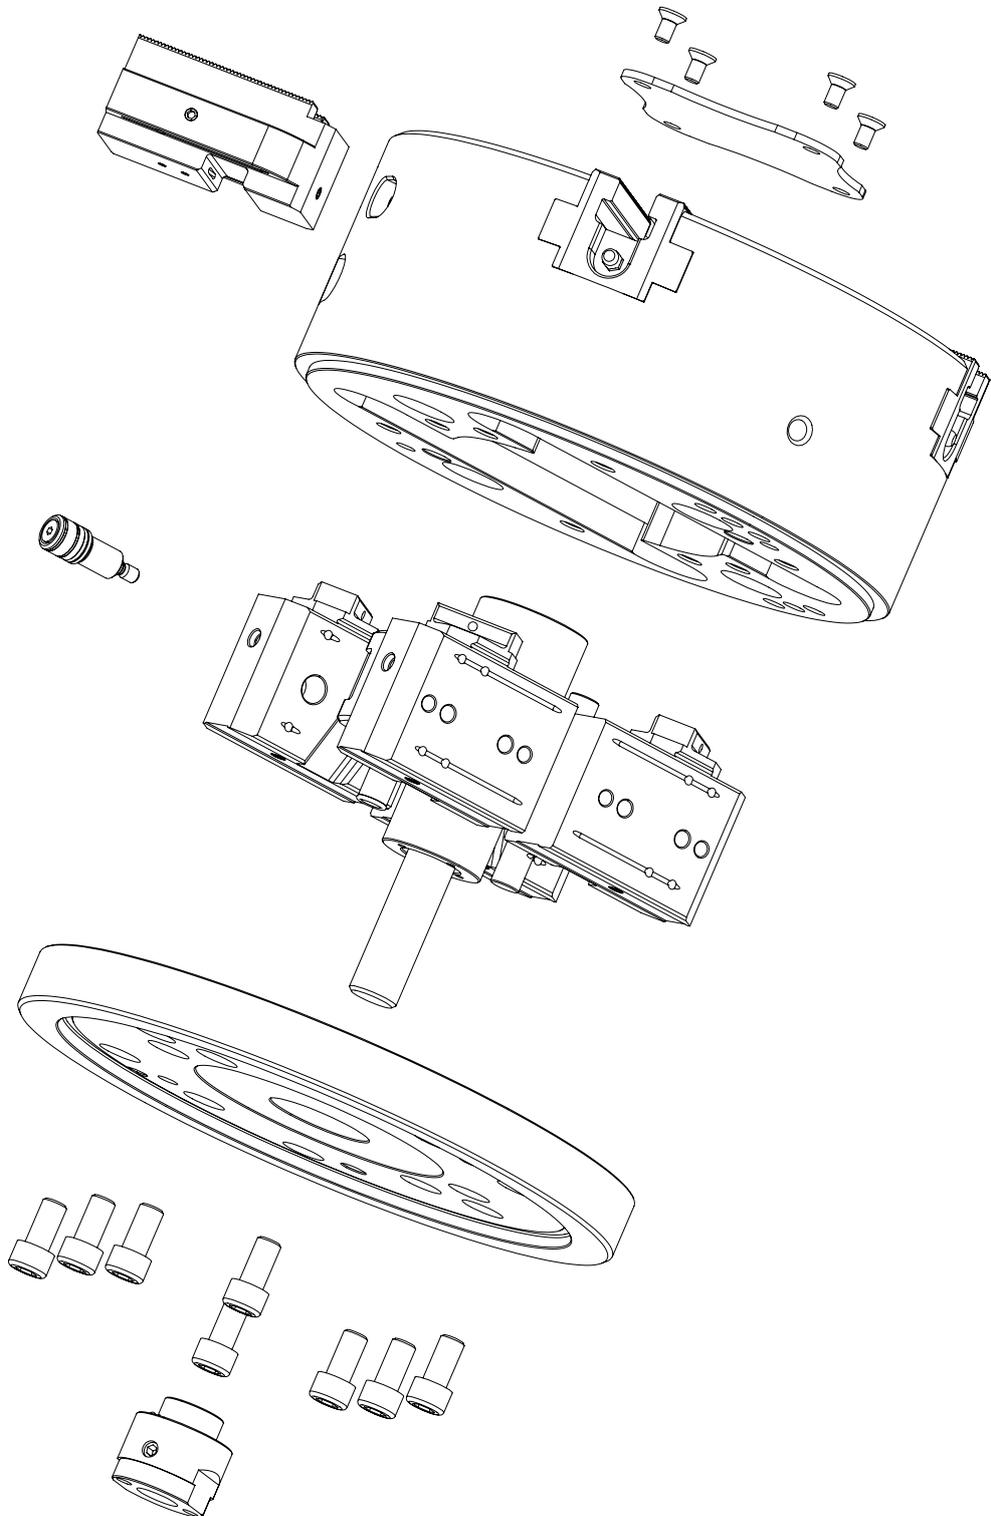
Smontaggio / montaggio del mandrino di serraggio (VK021 – VK080)
